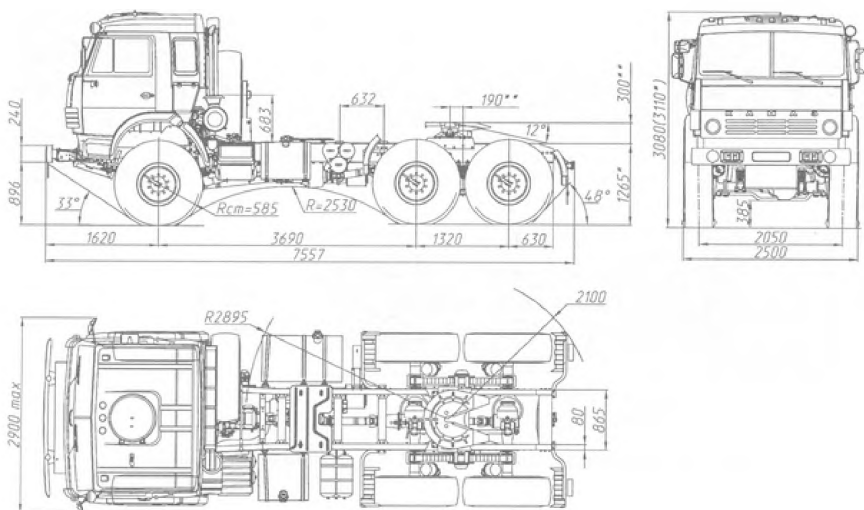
Автомобиль-тягач седельный КАМАЗ-53504. Габаритные размеры
